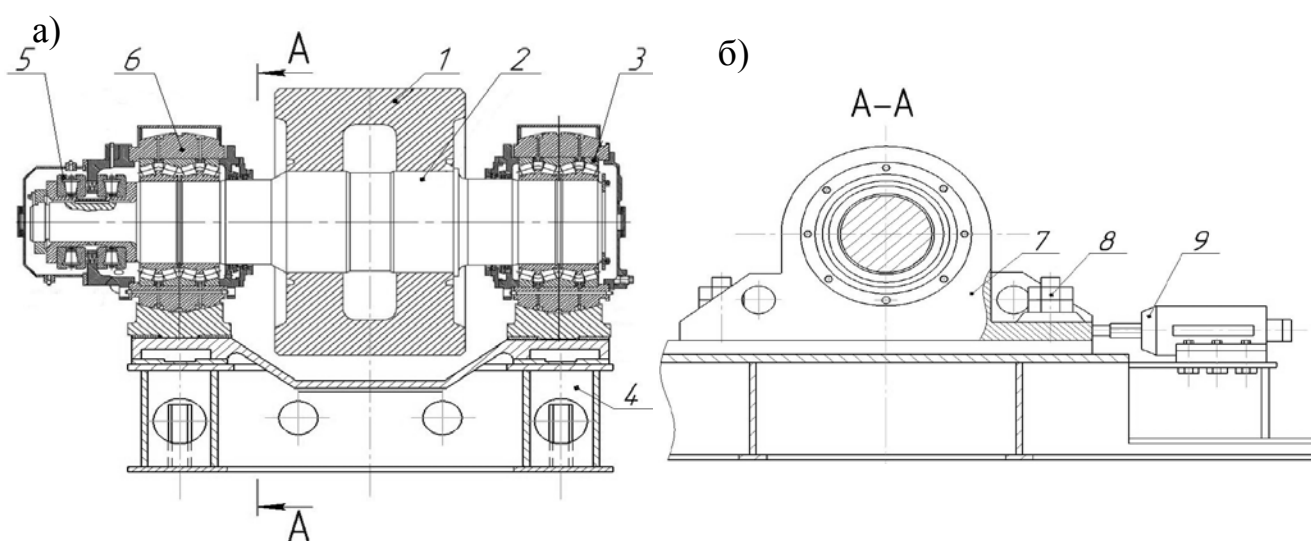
Конструкция роликоопоры: 1 – опорный ролик; 2 – ось; 3 – конические роликоподшипники; 4 – рама; 5 – упорные роликоподшипники; 6 – сферические вставки; 7 – корпус подшипников; 8 – крепежные детали; 9 – упор
